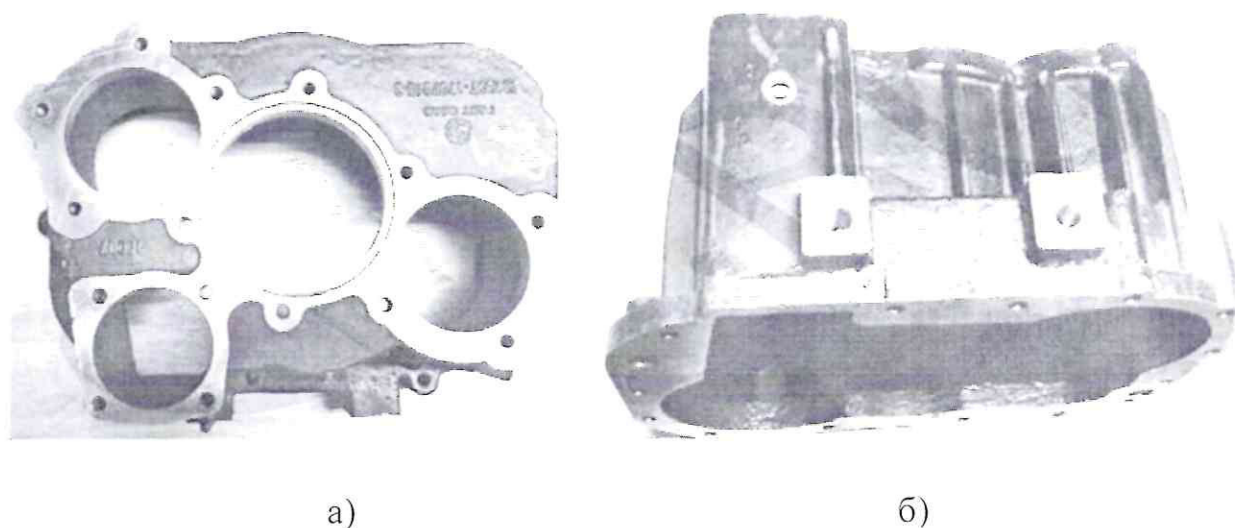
Корпус задней крышки КПП RTD RTD-11609-1707015; а) вид сверху; б) вид сбоку
